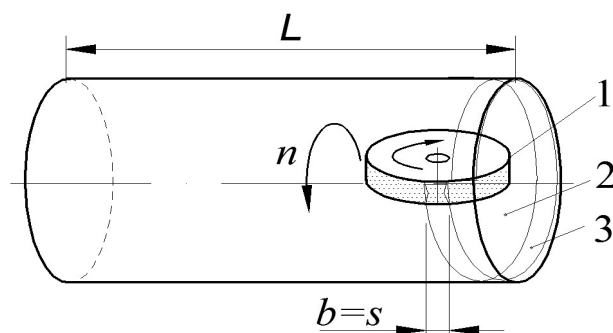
Схема обработки внутренней поверхности цилиндра:
